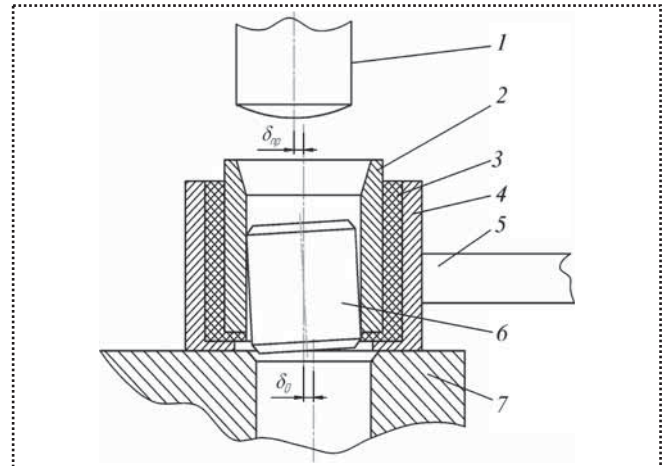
Роботизированный комплекс запрессовки цилиндрических деталей в отверстия собираемого узла
